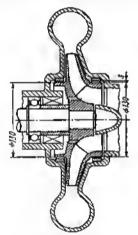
Rotor de élabes con fuerza axial de presión hidroestática equilibrada
